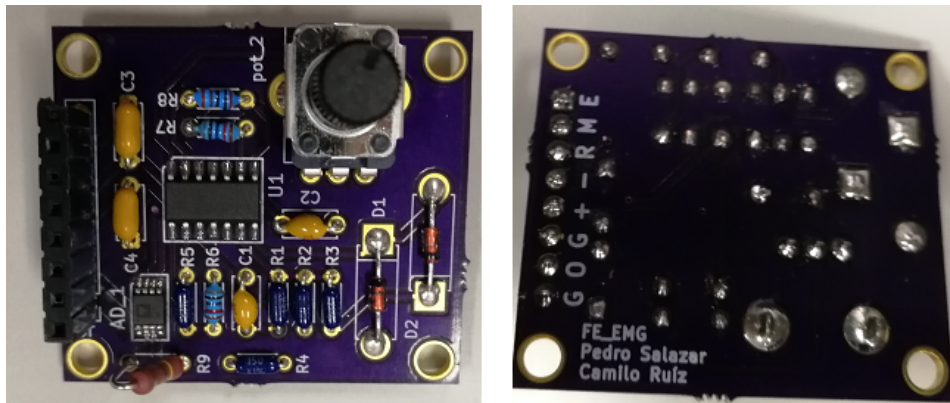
PCB fabricada por Osh Park con los componentes soldados en cara superior y cara inferior. (vistas superior e inferior)
